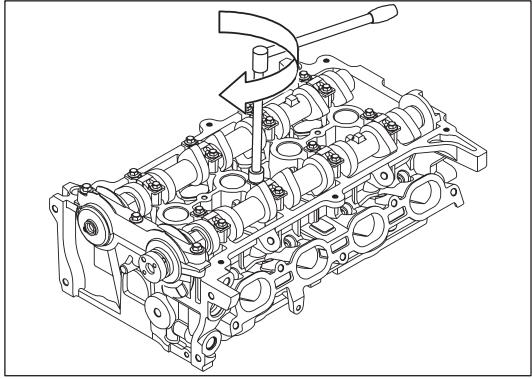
Установка крышки подшипника распределительного вала
